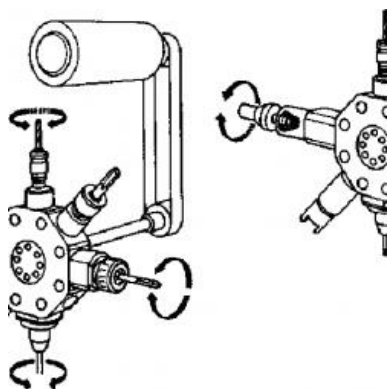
Конструктивная схема револьверной головки с вращающимися шпинделями токарного станка
